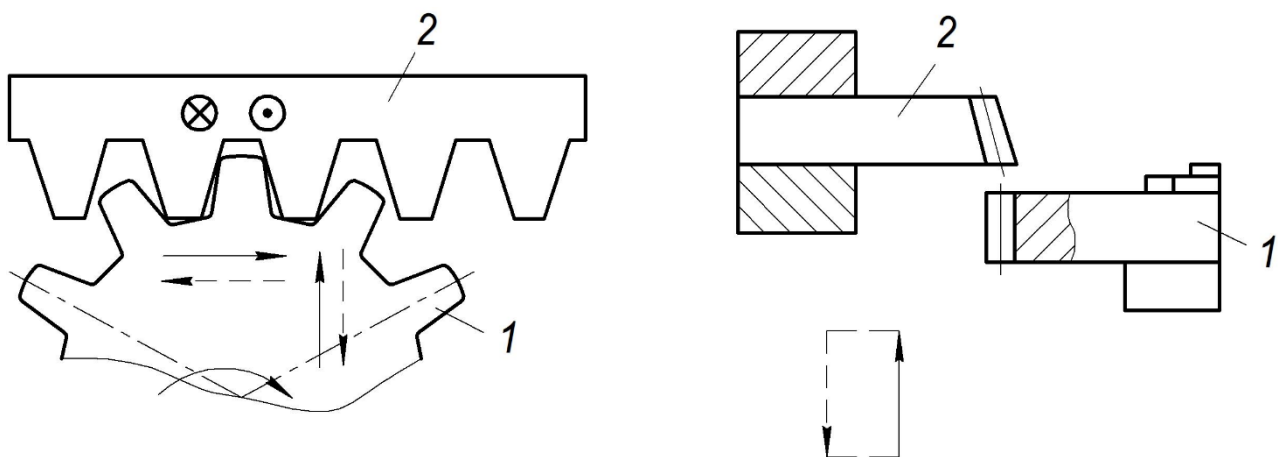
Схема нарізування зубів коліс зубчастими гребінками:
